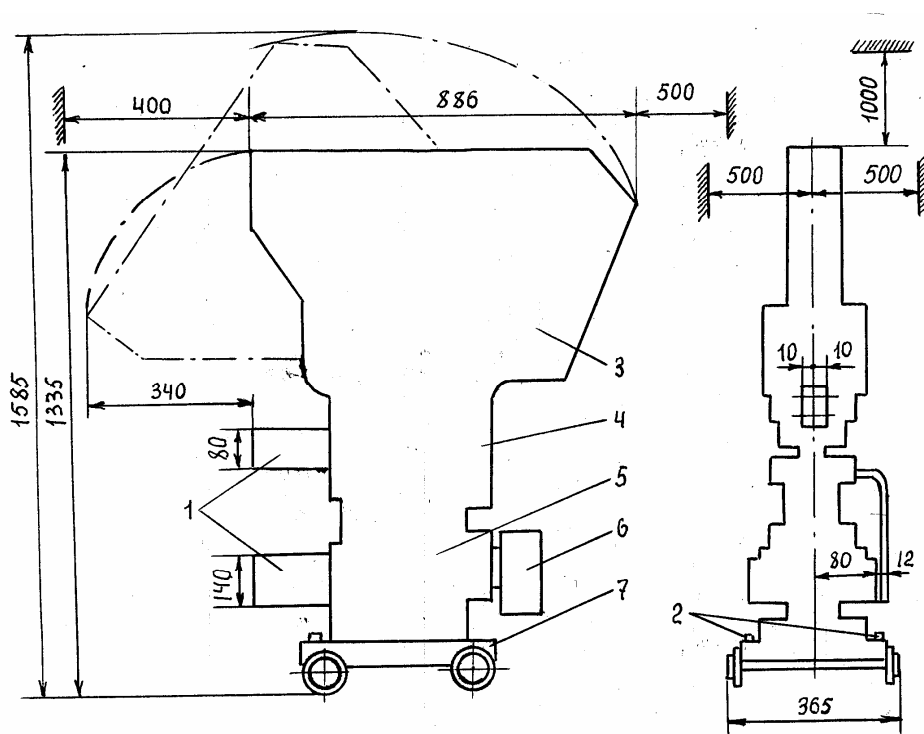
Выключатель автоматический быстродействующий катодный ВАБ-43-4000/10-К: 1 – выводные шины; 2 – болт заземления; 3 – дугогасительная камера; 4 – блок главных контактов; 5 – электромагнитный механизм; 6 – блокировочные контакты; 7 – тележка
